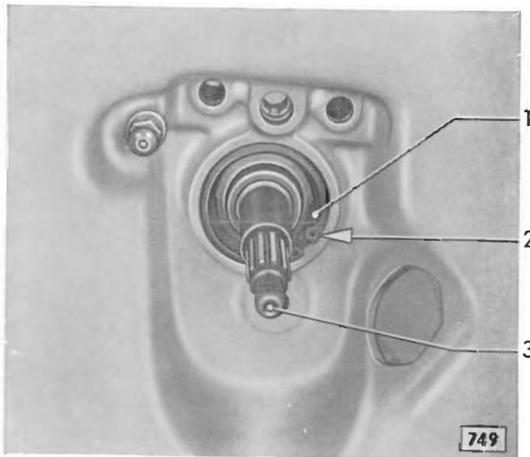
Hauptantriebrad in Getriebegehäuse eingebaut
